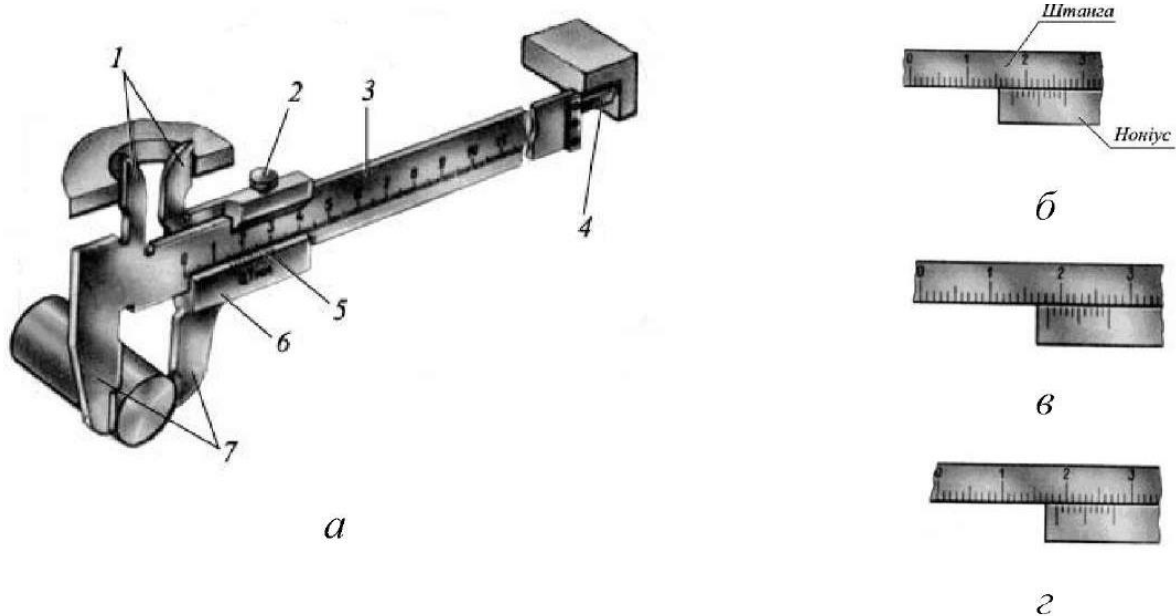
Приклад вимірювання деталей за допомогою штангенциркулю: а — вимірювання елементів деталей штангенциркулем ШЦ-1; б — розмір вимірювальної величини 18 мм; в — розмір вимірювальної величини 18,2 мм; г — розмір вимірювальної величини 18,4 мм; 1 — губки для внутрішніх вимірювань; 2 — затиск; 3 — штанга; 4 — лінійка глибиноміра; 5 — шкала-ноніус; 6 — рамка; 7 — губки для зовнішніх вимірювань
